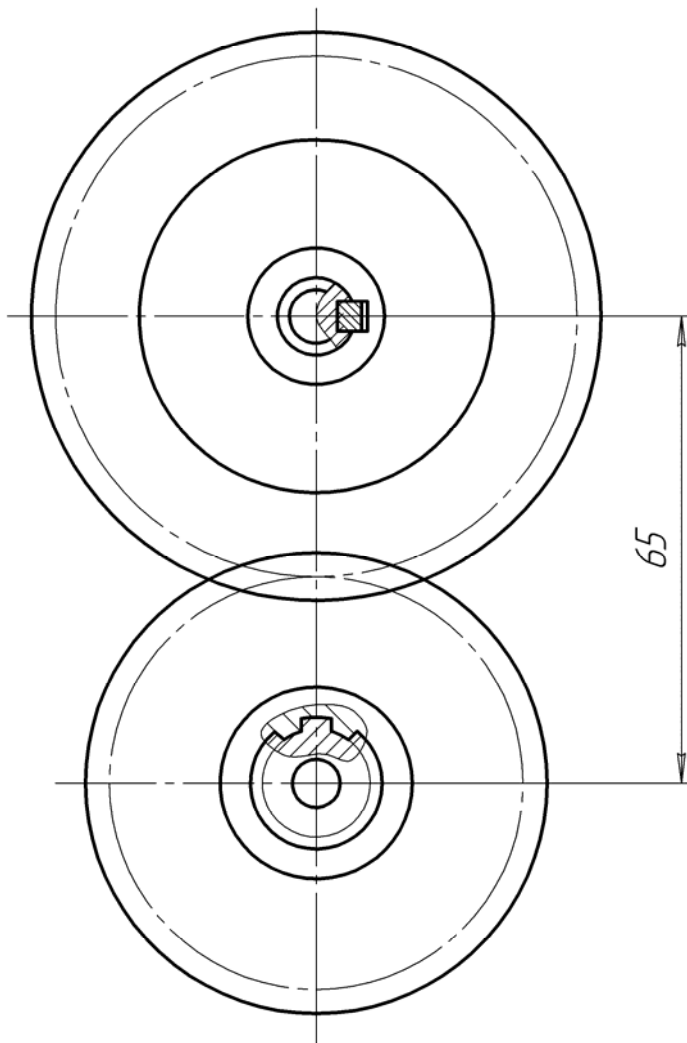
Сборочный чертеж зубчатой передачи со шпоночным и шлицевым соединением
